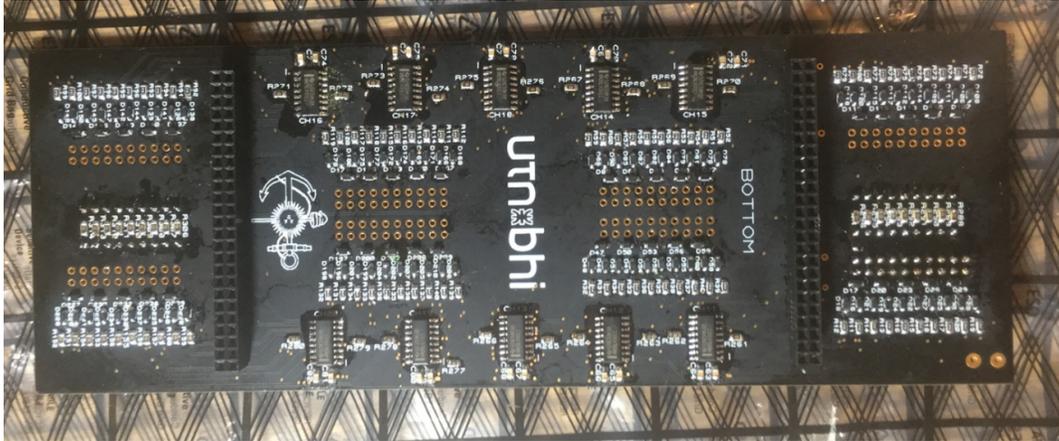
Proceso de soldado de la Daughter Board. Vista inferior.
